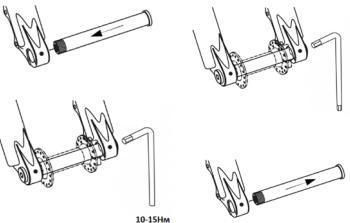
Установка колес, оборудованных втулкой «Thru axle»
